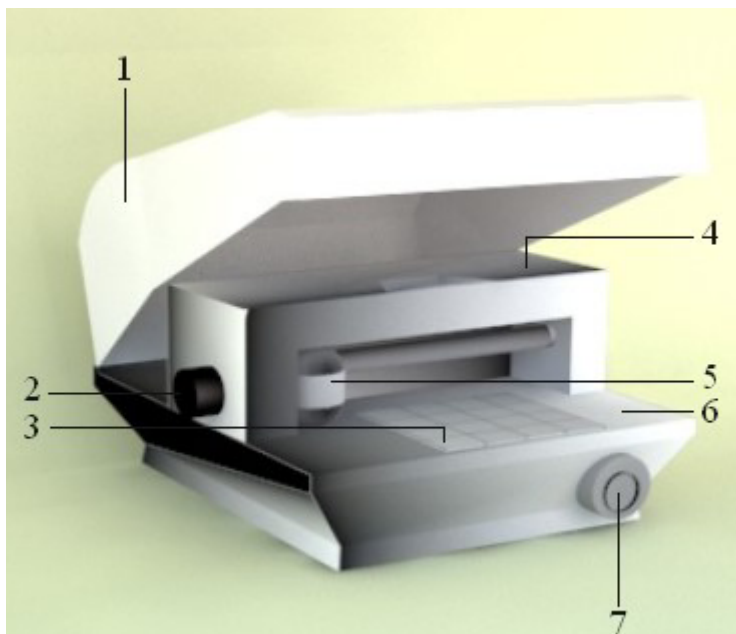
Механический ударный фотопринтер: 1 — крышка; 2 — винт (фиксирующий головку в определенном положении); 3 — липкий лист (на этом материале устанавливаются заготовки, которые исключают необходимость использовать двухсторонний скотч для закрепления); 4 — каретка (устанавливает головку на поверхности заготовки, перемещается вправо-влево и опускается вверх–вниз); 5 — головка; 6 — стол; 7 — кнопка включения питания.
